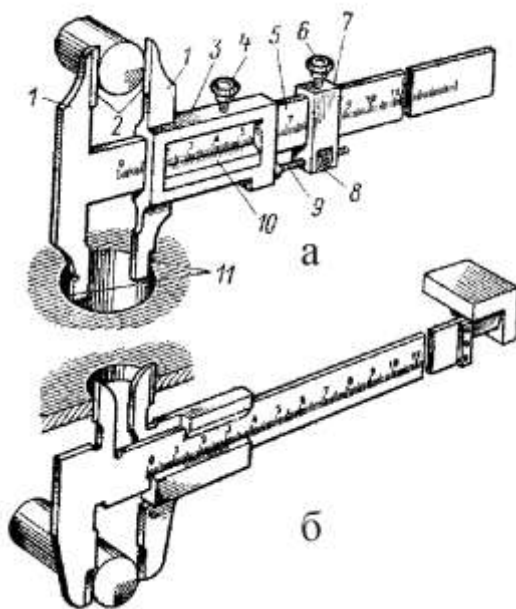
Конструкції штангенциркулів: а – ціна поділки – 0,05 мм; б – ціна поділки – 0,1 мм; 1 – губка; 2 – вимірювальна площина; 3 – рамка ноніуса; 4, 6, 9 – гвинти; 5 – штанга; 7 – хомутик; 8 – гайка; 10 – ноніус; 11 – вимірювальна поверхня для контролю внутрішніх розмірів
